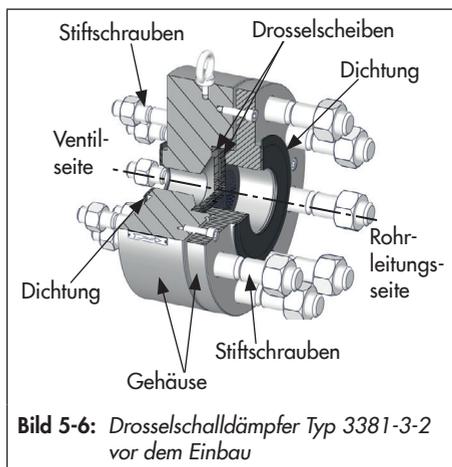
Drosselschalldämpfer Typ 3381-3-2 vor dem Einbau
